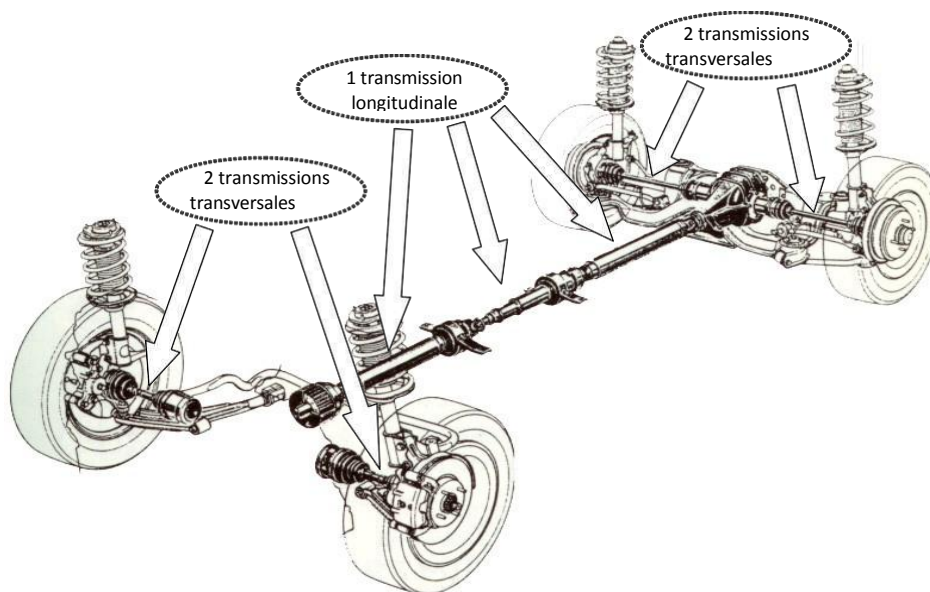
Ensemble des transmissions pouvant équiper un véhicule
